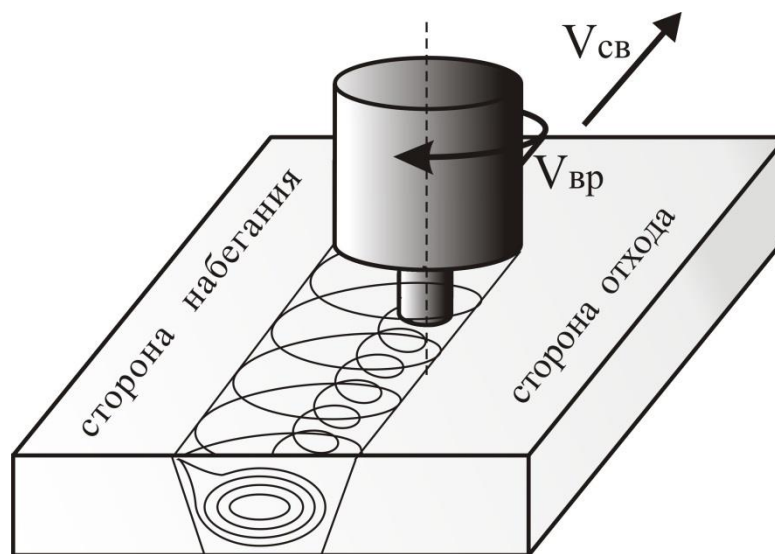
Сущность сварки трением с перемешиванием
